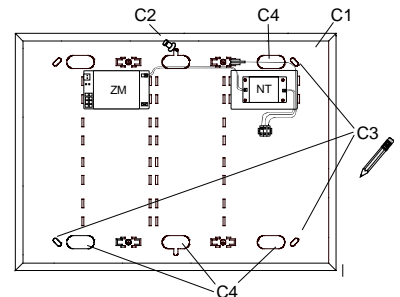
Anzeichnen der Bohrpositionen DIN A2
